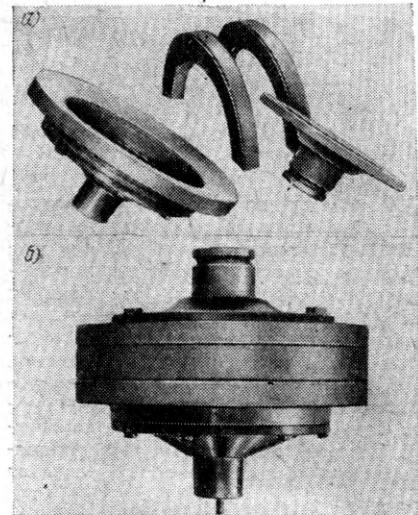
Приспособление для автоматической наплавки изношенной рабочей поверхности сердечника ведущей полумуфты (в разобранном состоянии); б) то же приспособление в сборе с одной половиной сердечника, подготовленное к постановке на станок для автоматической наплавки изношенной поверхности сердечника
